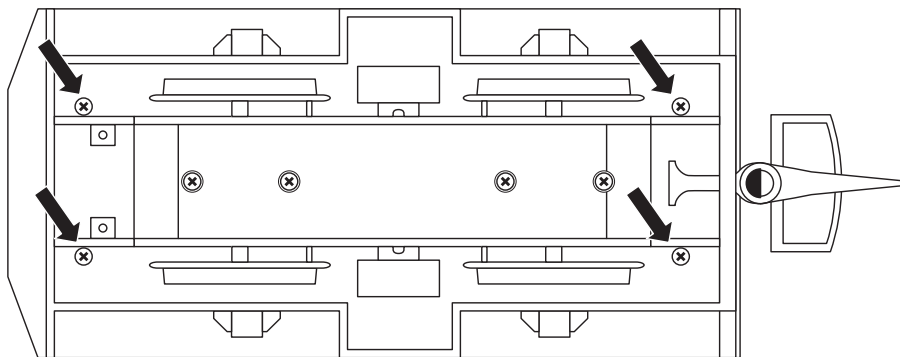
, zum Öffnen des Tenders die markierten Schrauben entfernen
